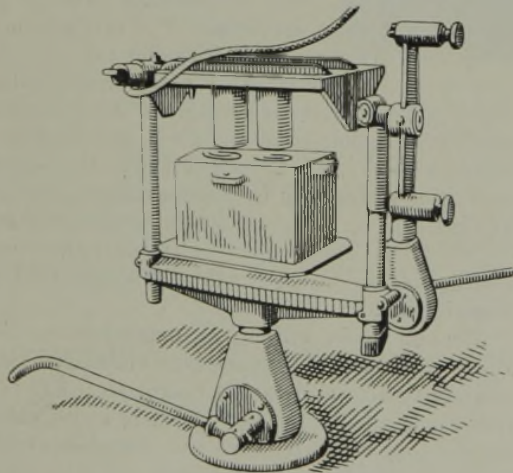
Wendeplattenformmaschine für Kolbenringbüchsen.
